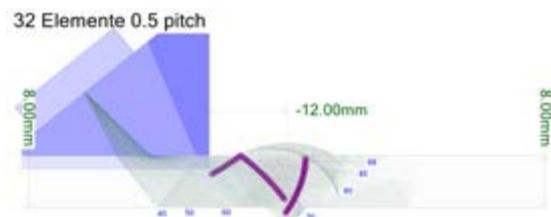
e. LOW-Profile-PAUT-Prüfkopf (16 mm Aperturlänge) auf 8 mm Wanddicke
